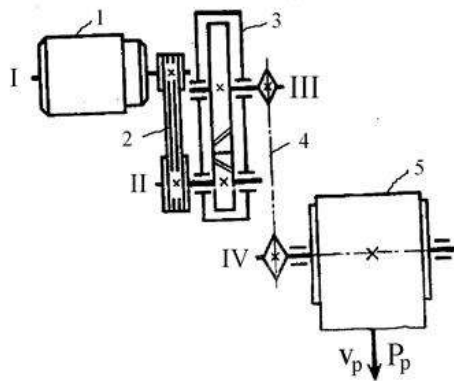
Кинематическая схема привода: 1 – двигатель, 2 – клиноременная передача, 3 – закрытая зубчатая передача, 4 – цепная передача, 5 – барабан ленточного конвейера.
